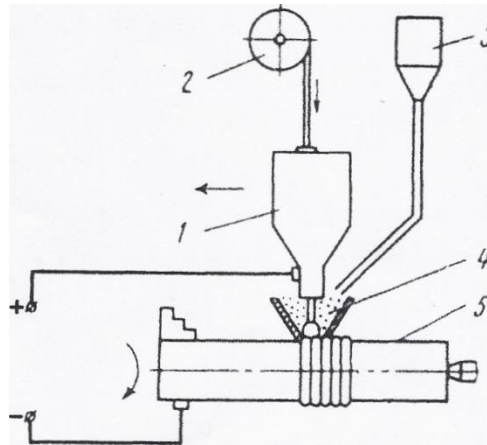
Схема електродугового наплавлення під шаром флюсу:
